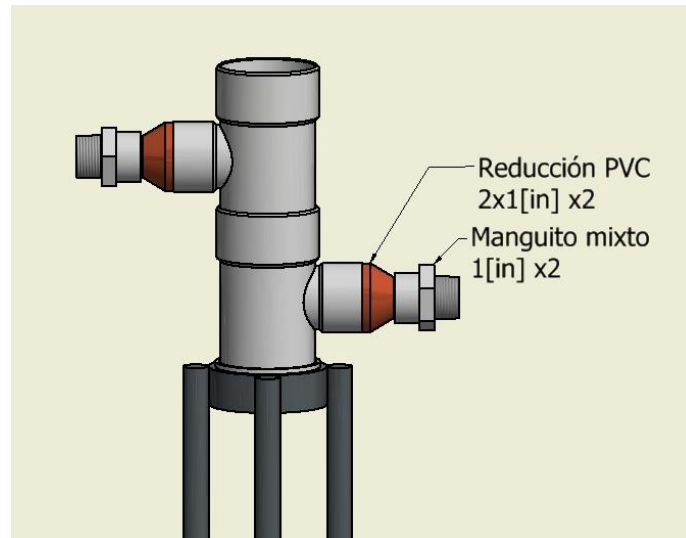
PRIMER PASO DE CONSTRUCCIÓN DE LA BOMBA
